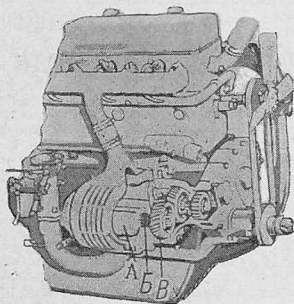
Один из способов расположения компрессора Рутта на четырехцилиндровых бензиновых двигателях.
